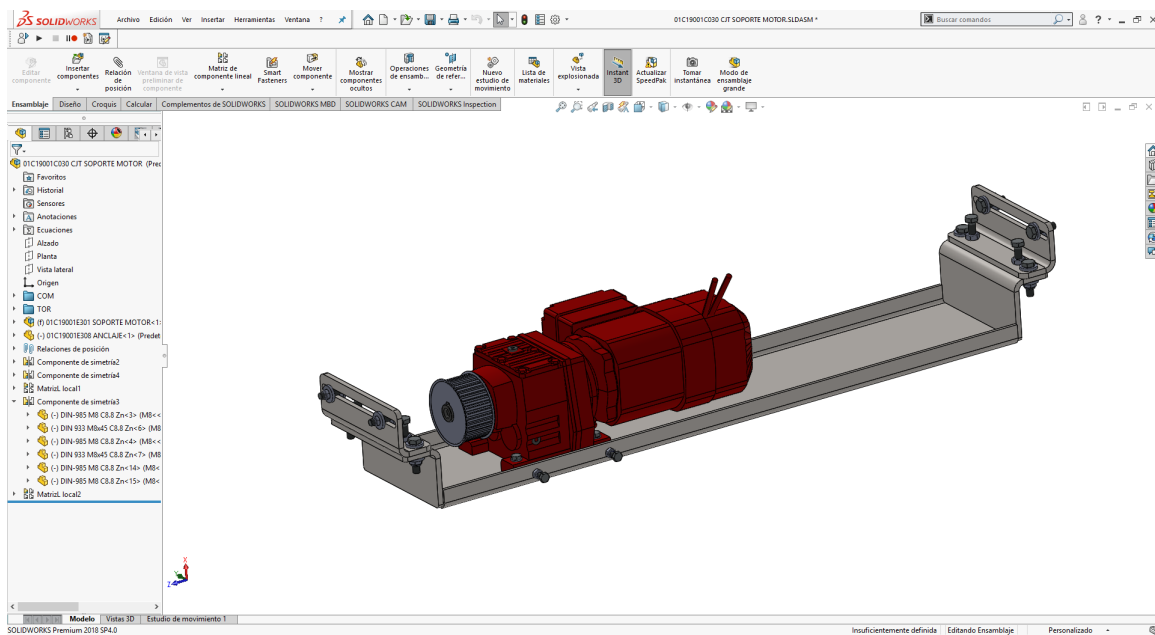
Esquema general y posiciones soporte motor, vista explosionada
